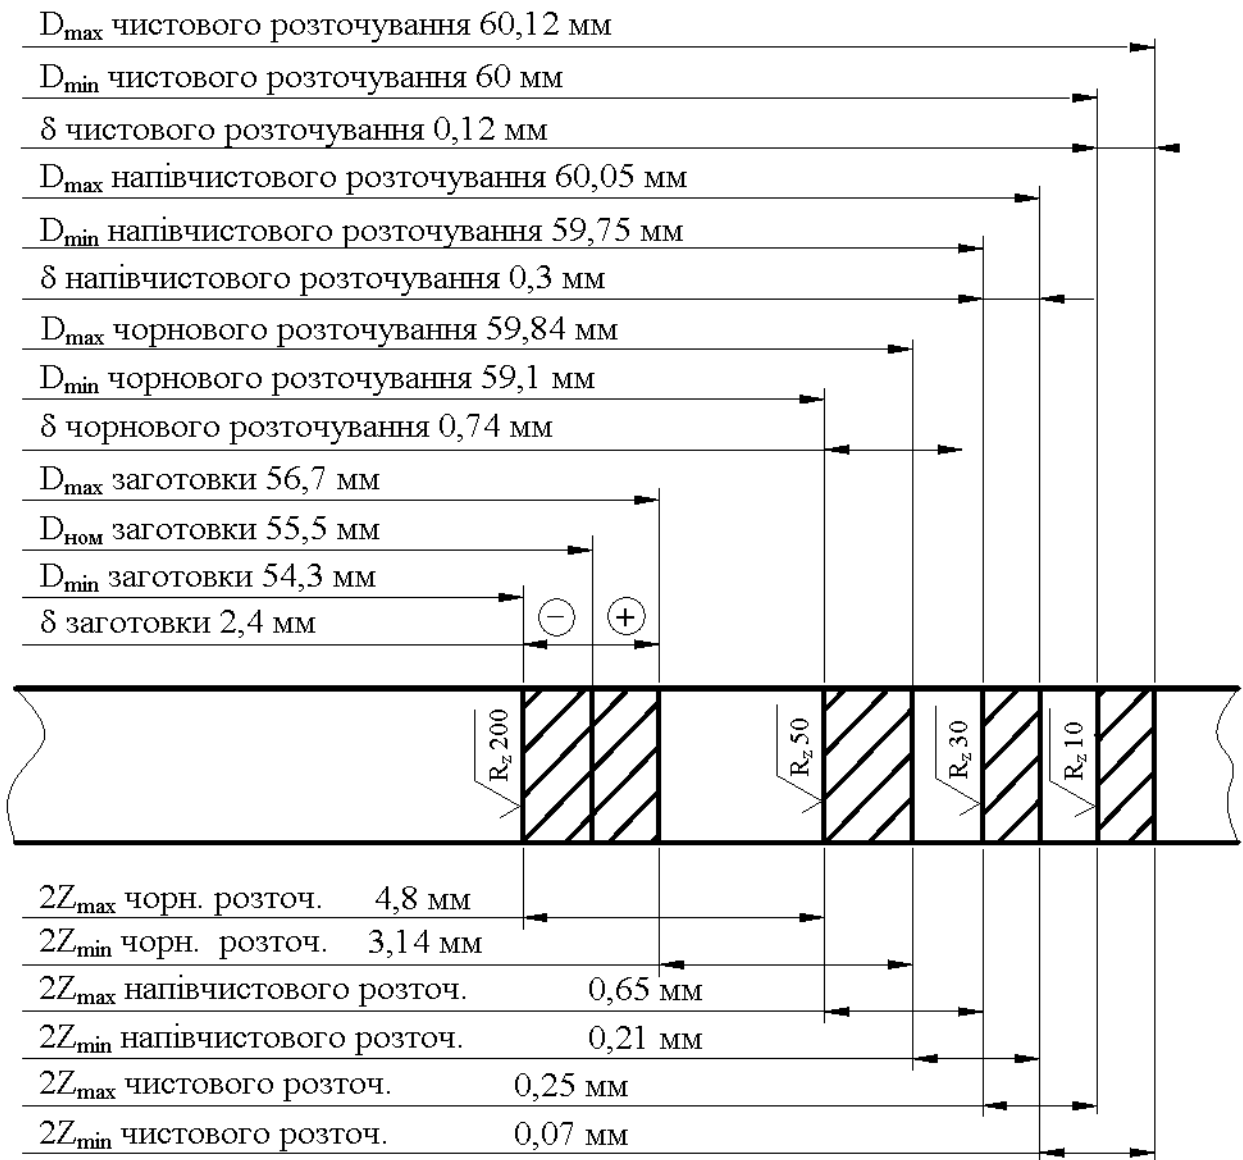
Схема графічного розташування припусків та допусків на обробку поверхні $\varnothing 60\text{H}10$
